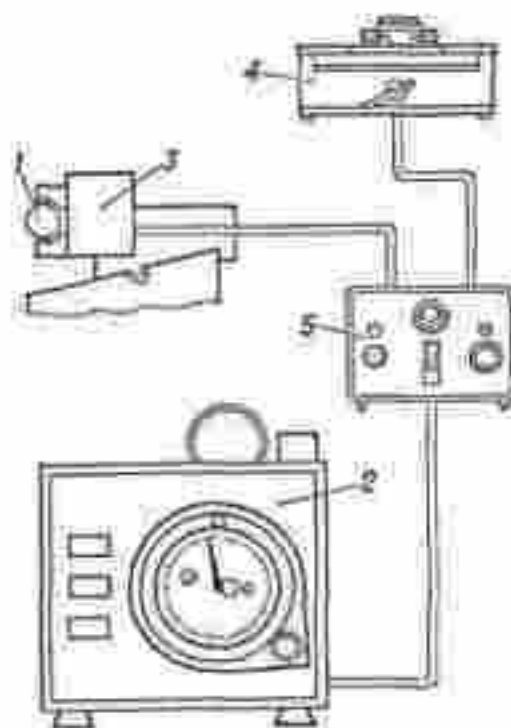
Схема прибора активного контроля для сопряжённого шлифования: 1 — обрабатываемая деталь; 2 — отсчётно-командное устройство; 3 — скоба для измерения диаметра вала в процессе обработки; 4 — измерительное устройство для определения диаметра отверстия, под которое обрабатывается вал; 5 — переключатель для подключения и отсчётно-командного устройства скобы (3) и измерительного устройства или совместного их включения.
